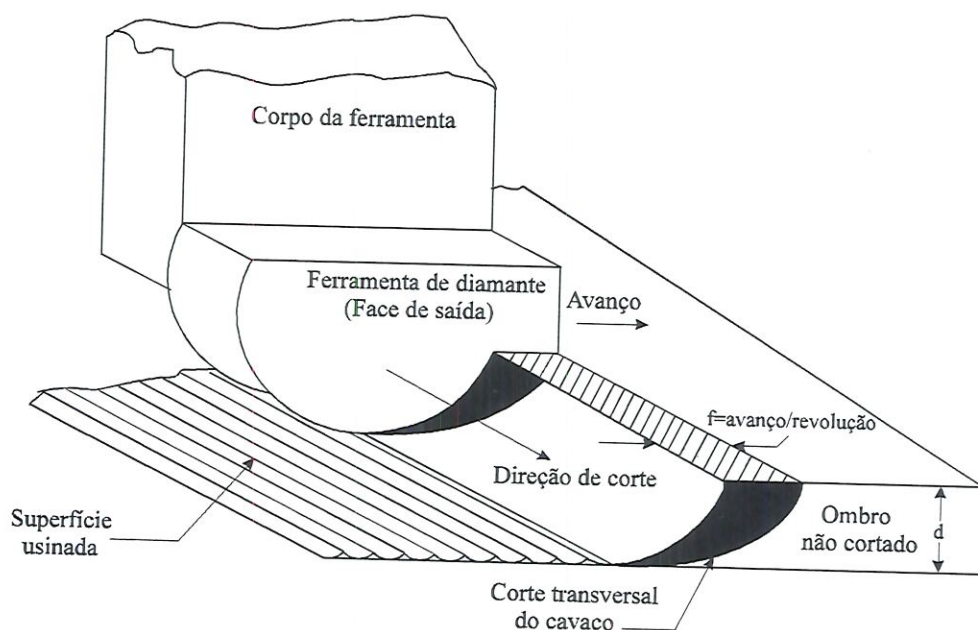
Geometria de corte para o torneamento com diamante com ferramenta com ponta arredondada. A combinação dos movimentos de corte e avanço produzem a seção transversal do cavaco projetada sobre o ombro não cortado (área escura)
